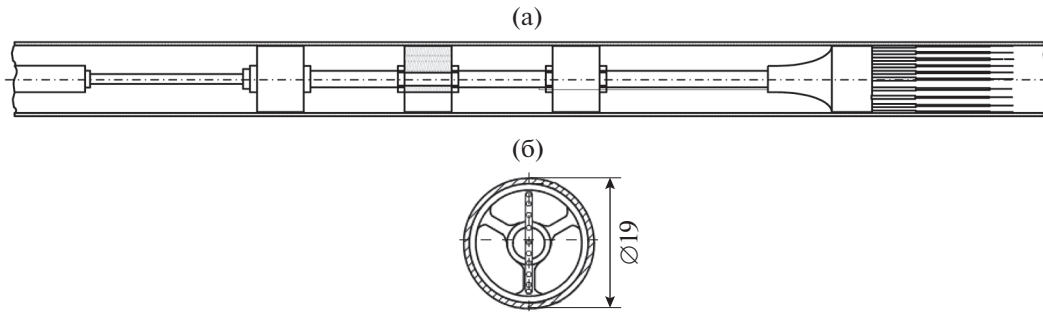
Продольный зонд типа “гребенка” для канала прямоугольного сечения: (а) – вид сбоку, (б) – вид с торца трубы рабочего участка.
